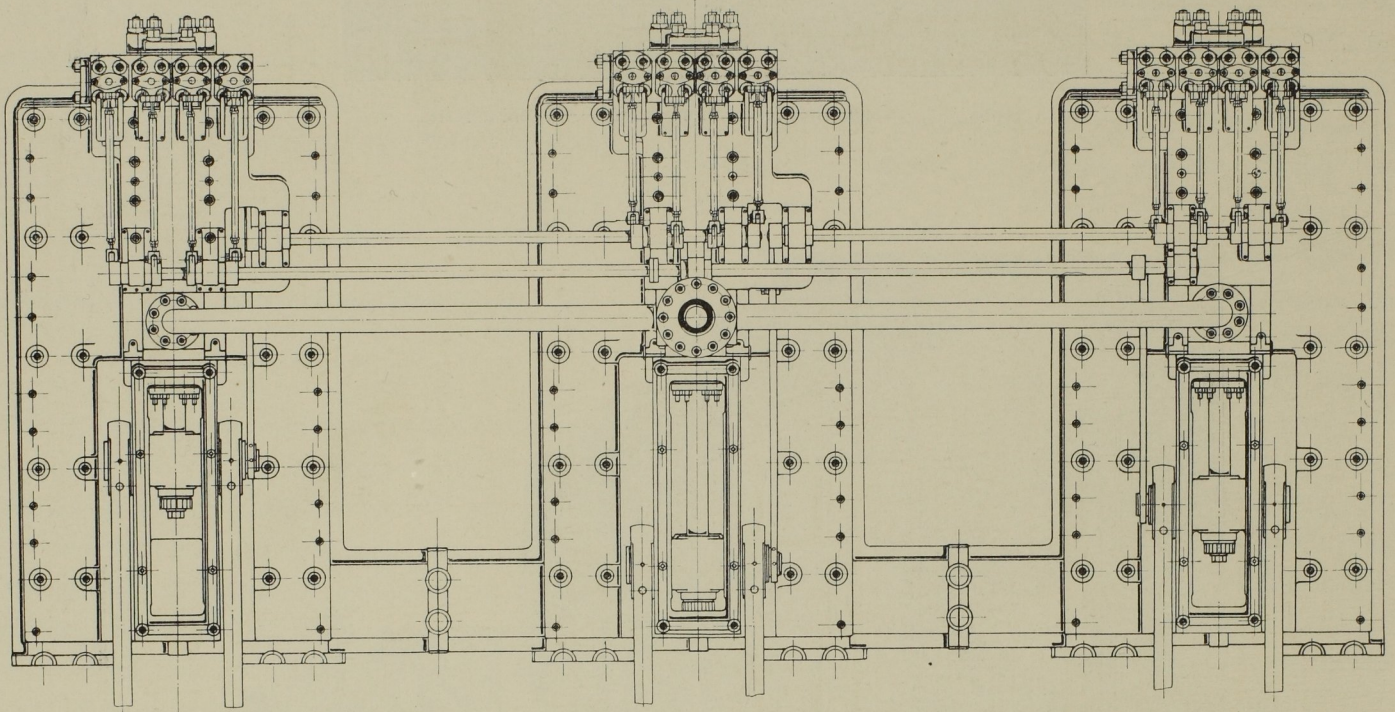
Grundriss der Presspumpen. Massst. 1:64.
